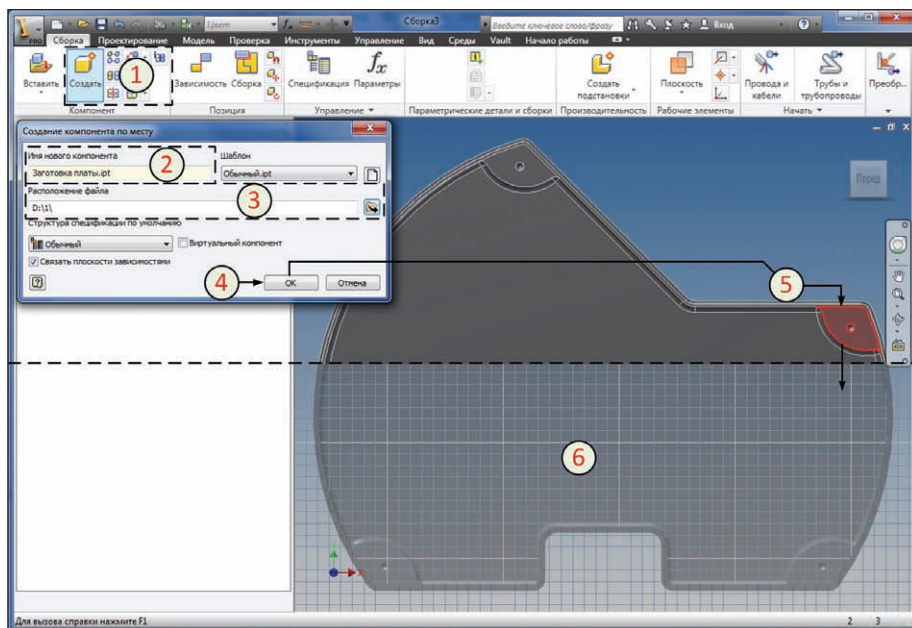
Создание новой детали – "заготовки" платы – в контексте сборки
